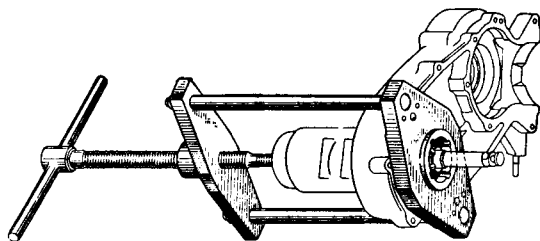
Приспособление для выпрессовки вторичного вала коробки передач
